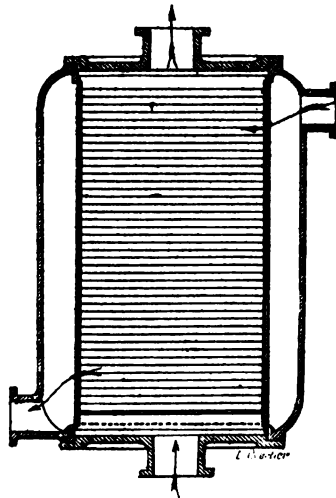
Condenseur à surface de Du Tremblay pour machines à vapeur combinées (1854).
